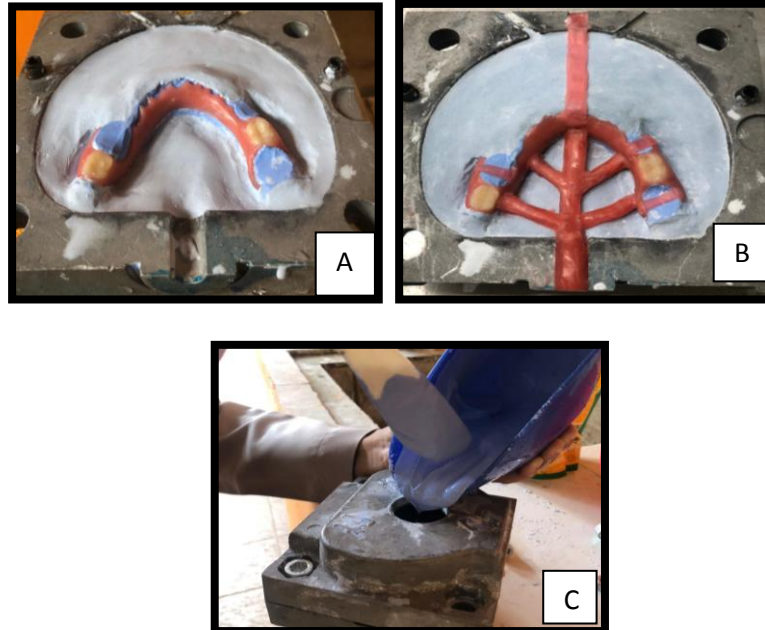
Penyusunan Elemen Gigi Tiruan dan Waxing
